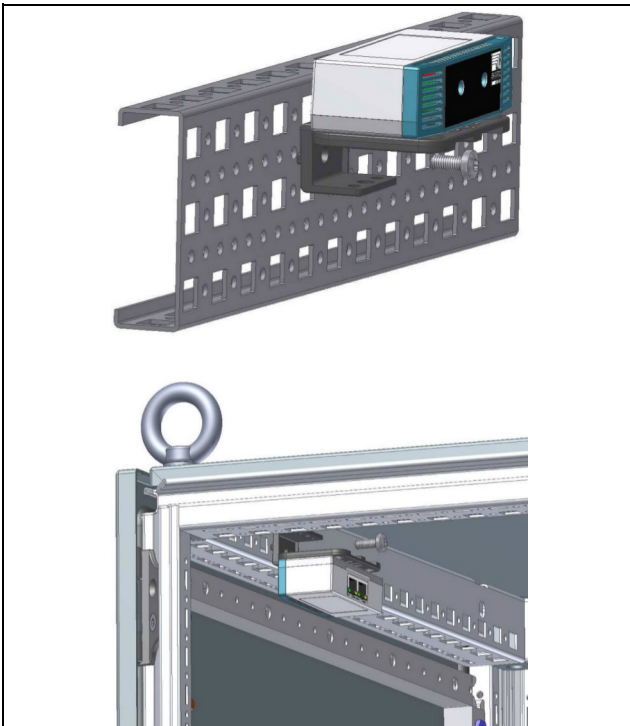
Befestigen des Sensors im Schaltschrank bzw. IT-Schrank
